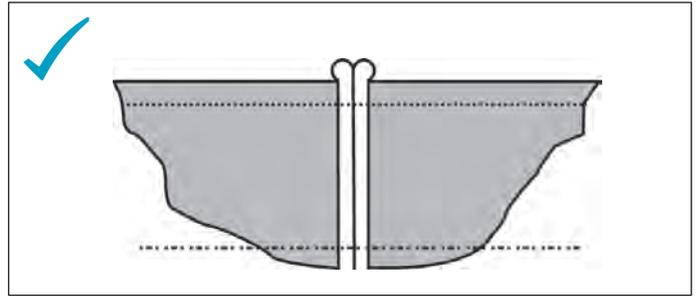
Cordón de soldadura con protuberancias excesivas (notable a suficiente)
